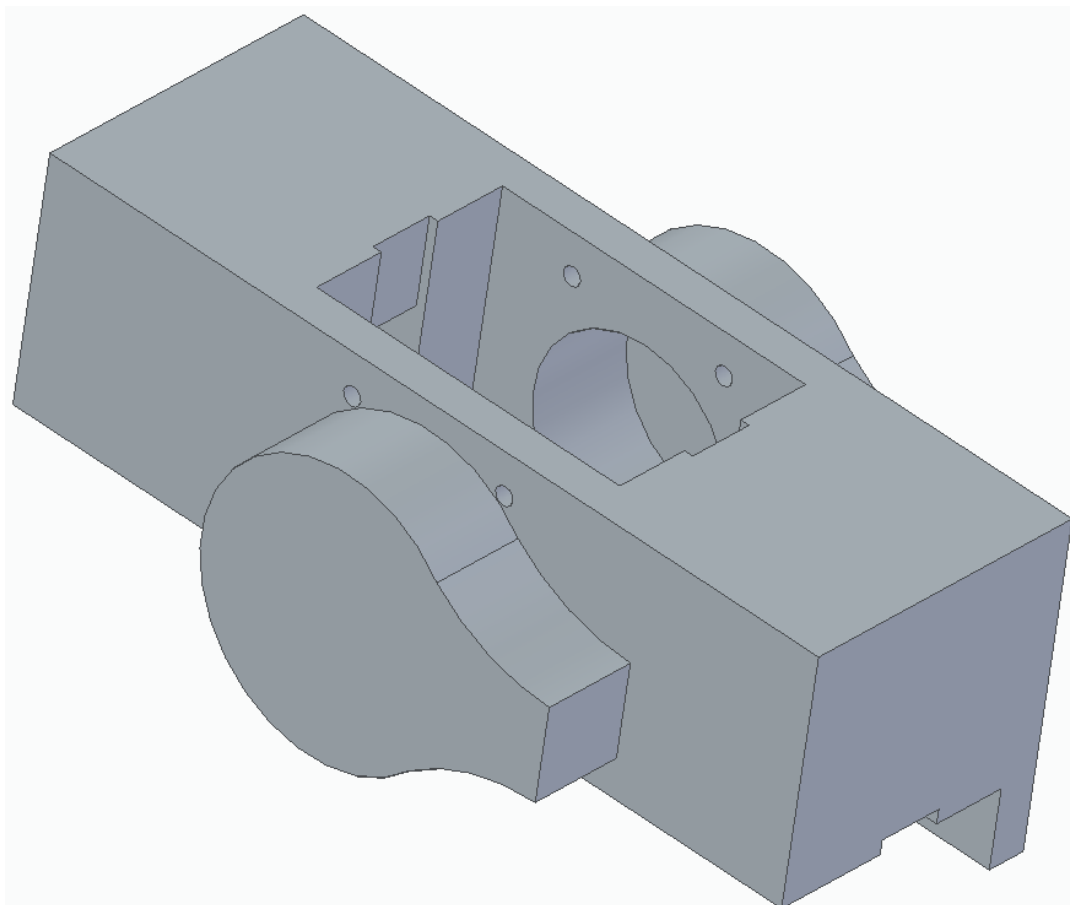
Vista de la pieza base 2. Fuente: elaboración propia
